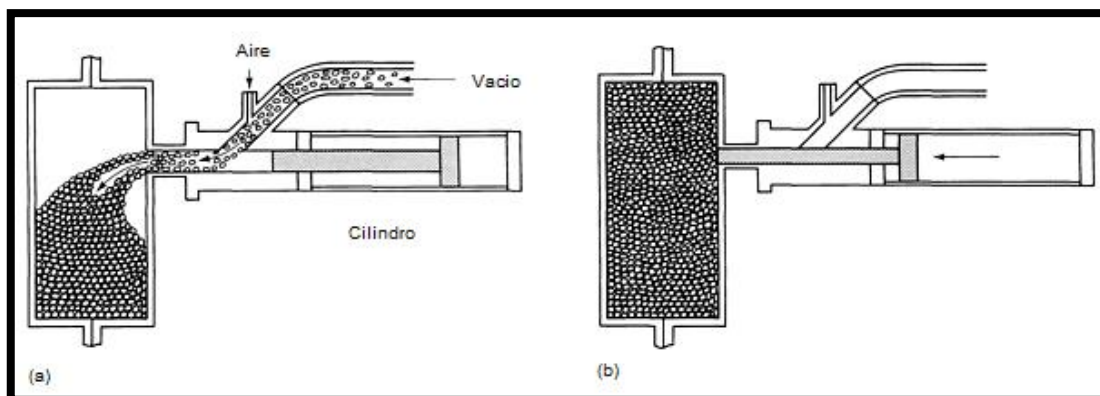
Llenado de EPS a la prensa de moldeo. (a) Transporte de material con aire. (b) Molde cerrado antes de la expansión. Fuente: [16, p. 506]
